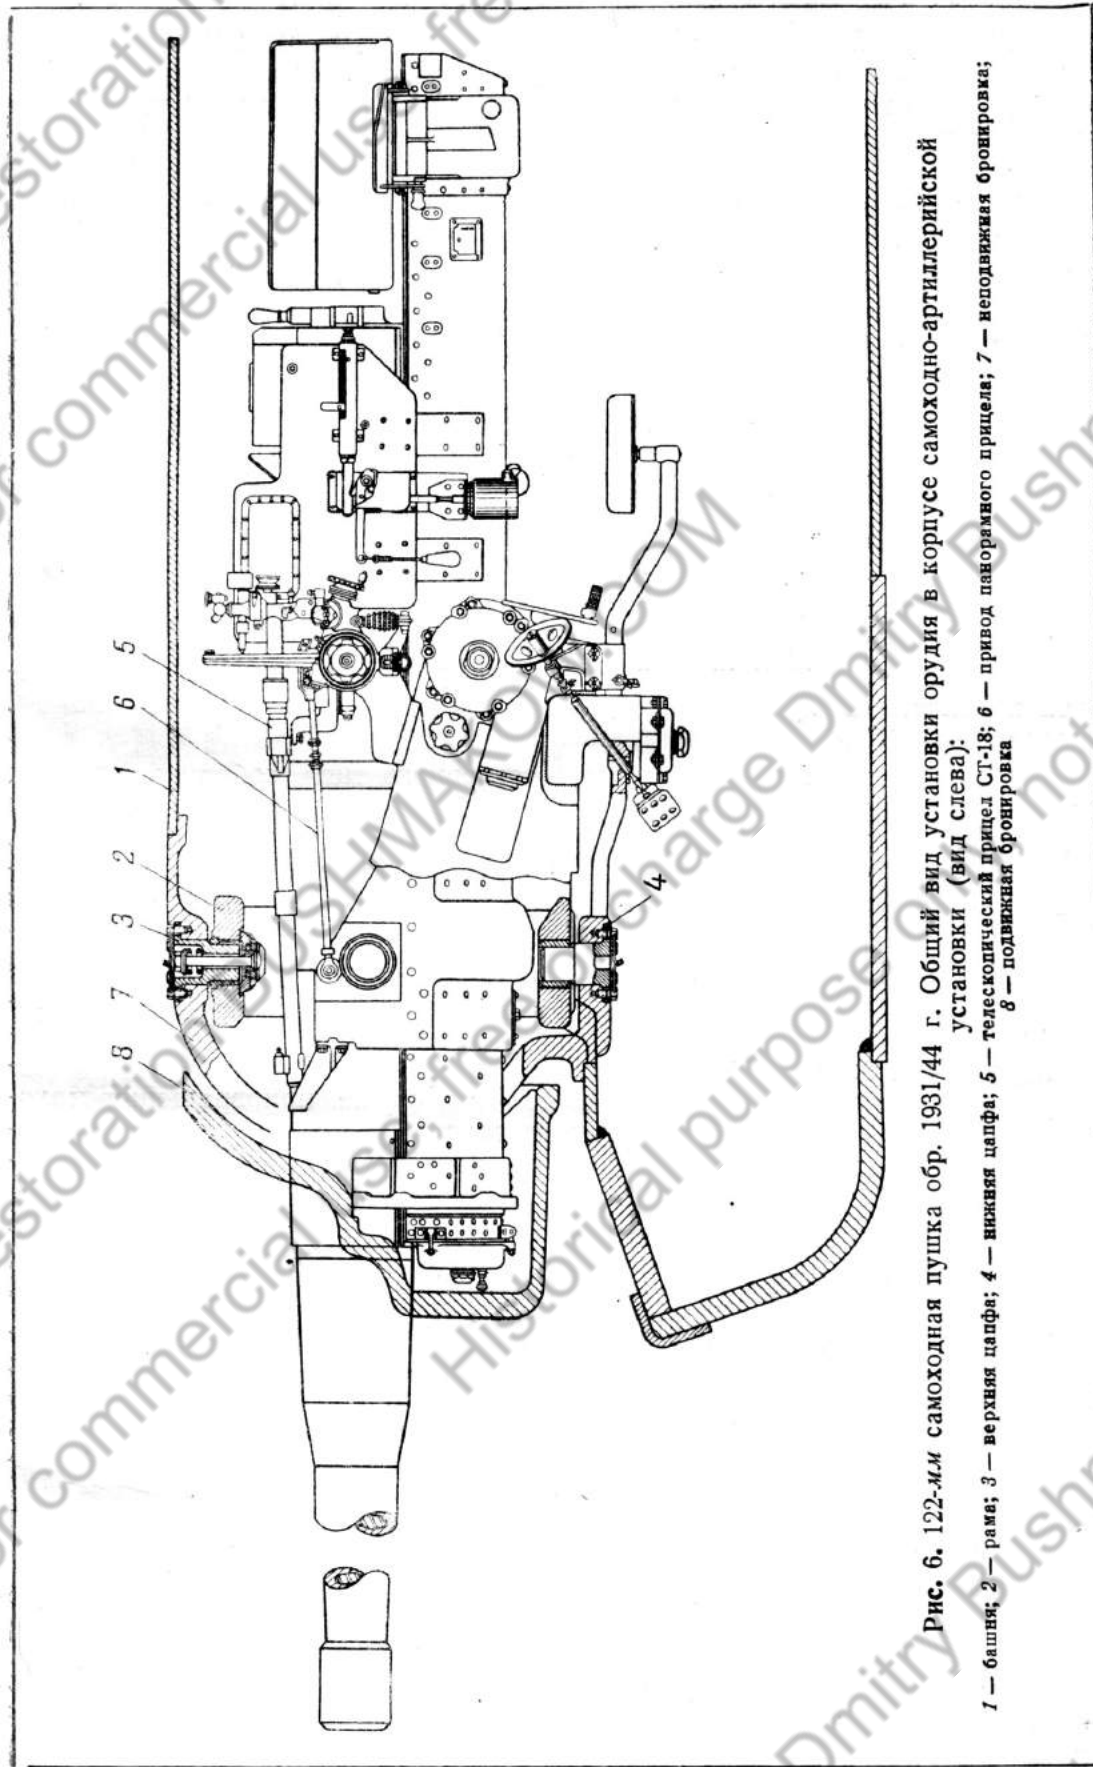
122-мм самоходная пушка обр. 1931/44 г. Общий вид установки орудия в корпусе самоходно-артиллерийской установки (вид слева):
